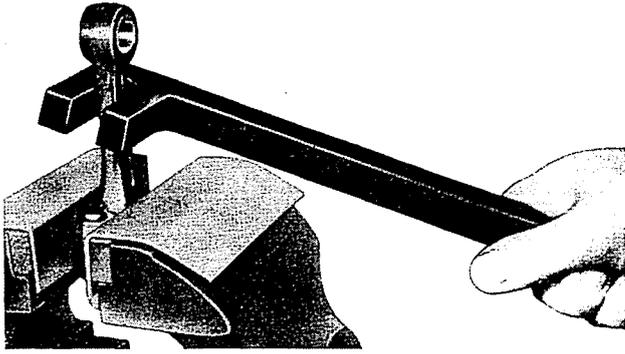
Pleuelstange mit Gabelhebel A. 10029 ausrichten.
